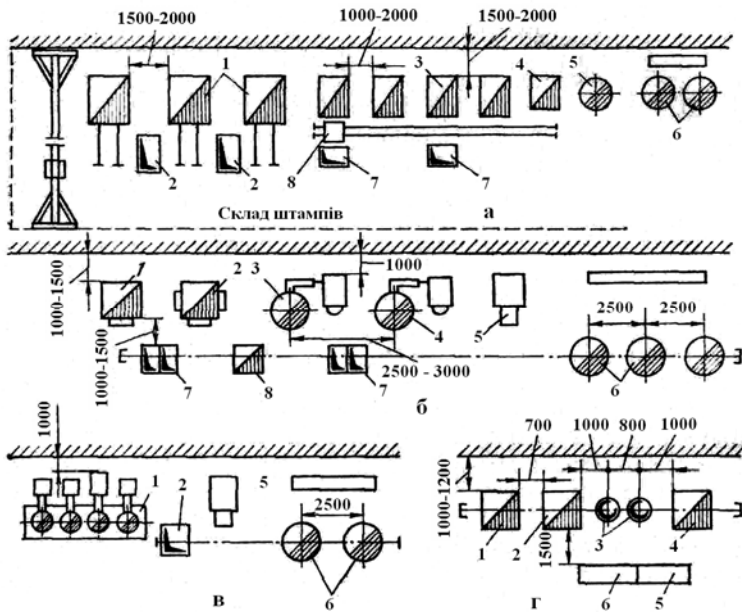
Плани окремих ділянок для термічної обробки інструменту: а – штампів, б – швидкорізальної сталі (перший варіант); в – швидкорізальної сталі (другий варіант); г – протяжок
